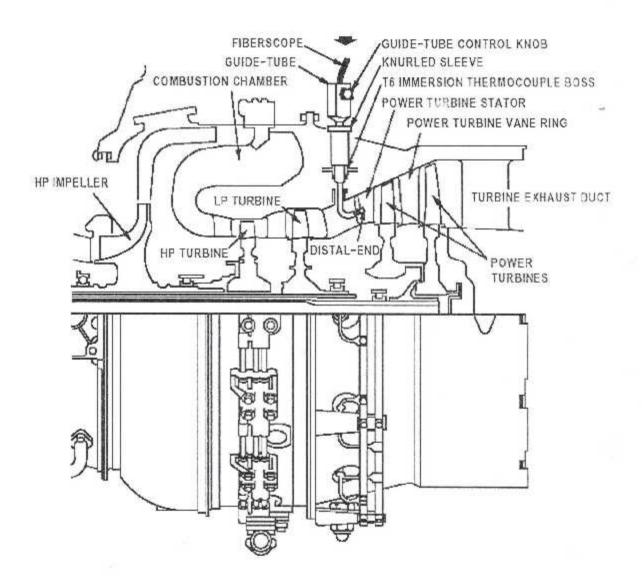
INSPECTION BOROSCOPIQUE DE L'ASSEMBLAGE STATOR ET LES AUBES DU 1^{ER} ETAGE DE LA TURBINE LIBRE
